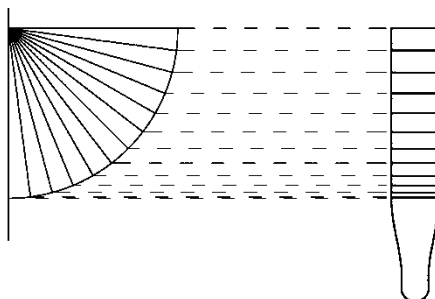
Construcción de la tablilla de pujas para trazar el arrufo de la cubierta.
